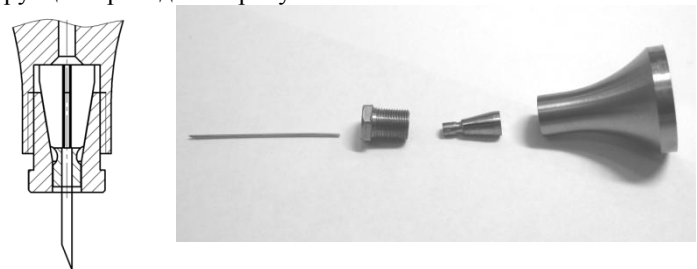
Пассивный рабочий инструмент для размерной обработки с цанговыми зажимами «обратного» типа
